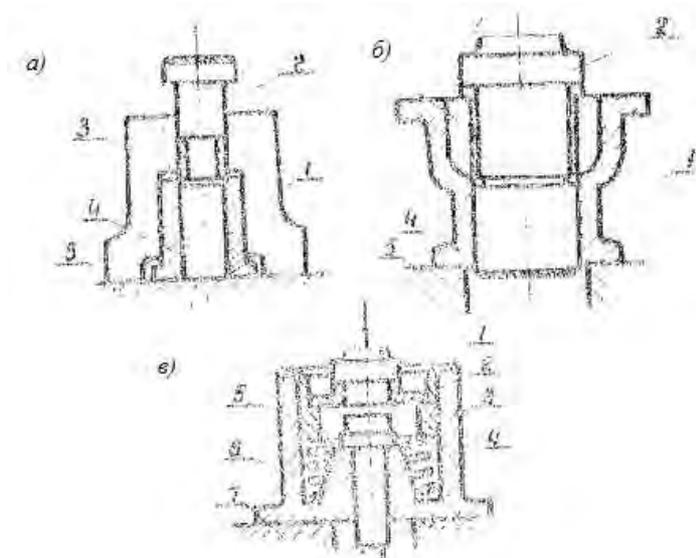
Схемы приспособлений к универсальным прессам.
